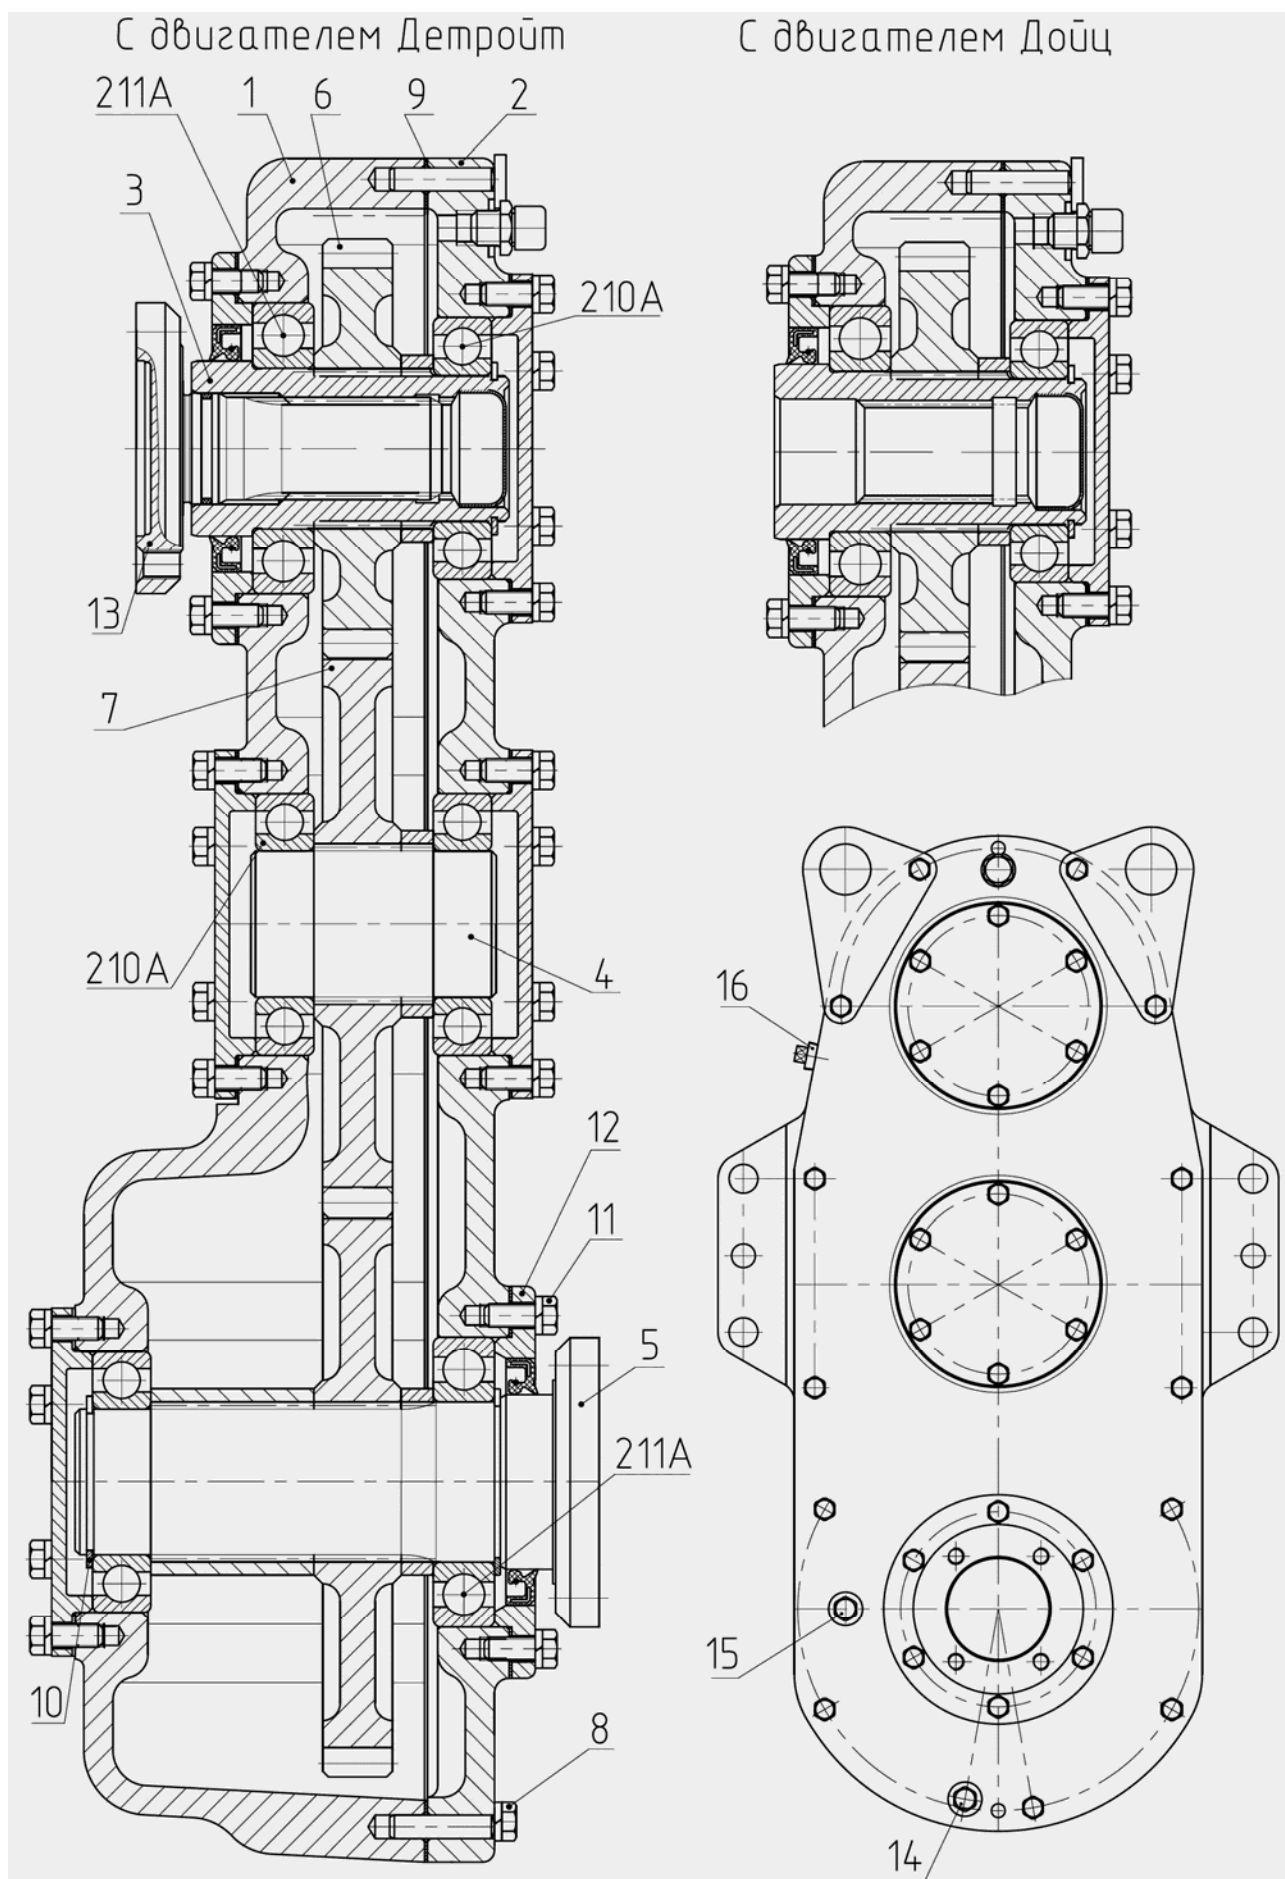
Редуктор ПВОМ 2822-4209010 и 2822-ДЦ-4209010.
